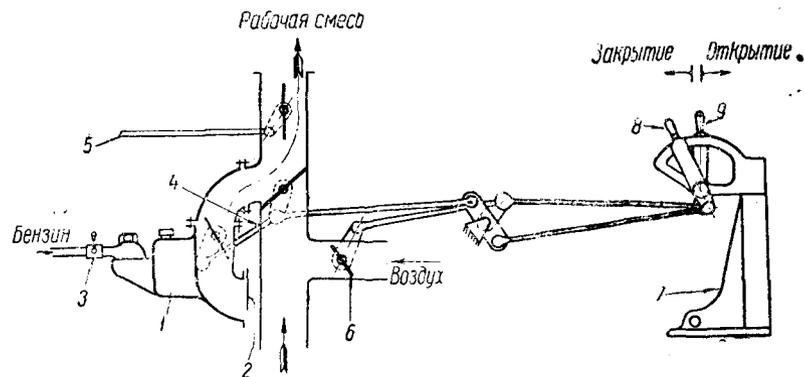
Схема расположения рычагов, поводков и тяг управления заслонками смесителя двигателя трактора «сталинец-60»:
